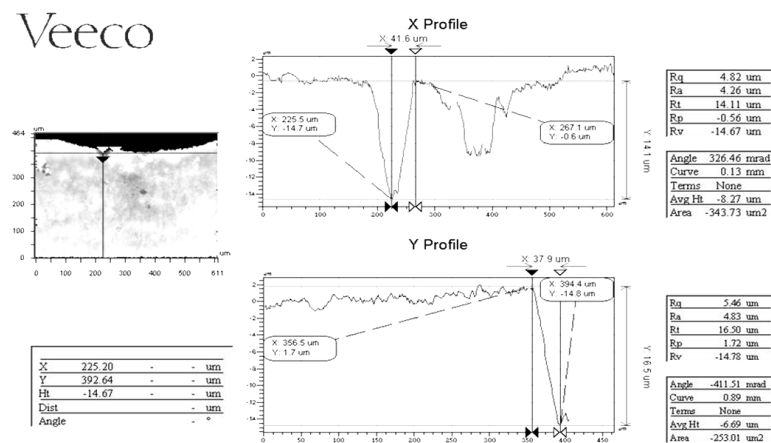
9 Profil 2D de la face de coupe d'un outil en coupe orthogonale.
